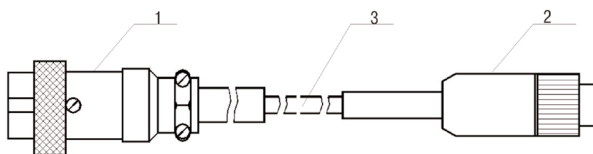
Кабель удлинительный для ЗВЛМ
